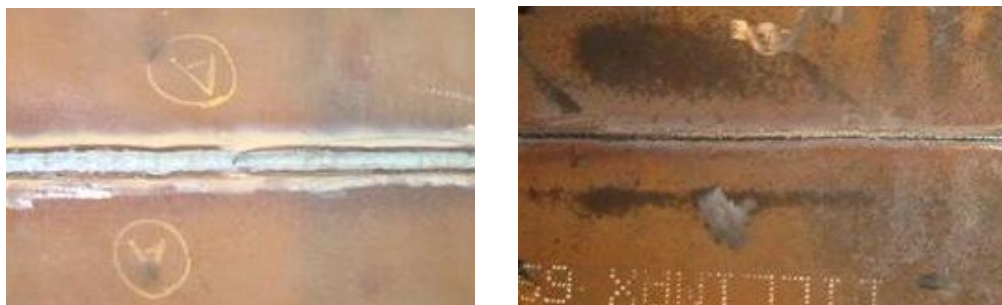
Soldadura com eléctrodo revestido e Soldadura com fio fluxado
